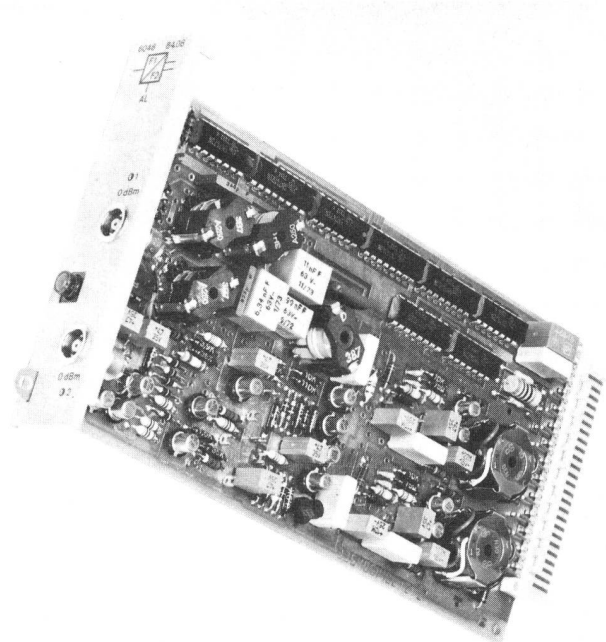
Baugruppe mit Frontplatte und koaxialen Messbuchsen, Alarmlampe und Funktionssymbol. Hinten: 25poliger ISEP-Stecker – Unité enfichable avec plaque frontale et prises coaxiales de mesure, lampe d'alarme et symbole de fonction. A l'arrière-plan: Prise ISEP à 25 pôles
